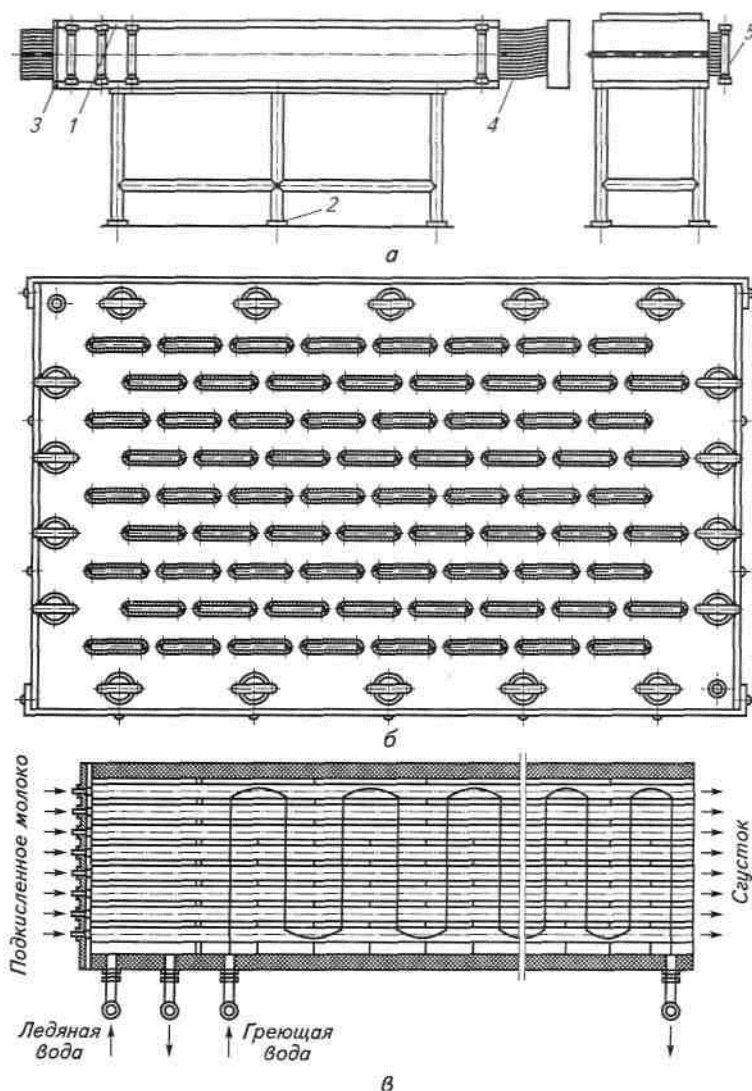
Трубчатый коагулятор: а - общий вид: 1 — корпус; 2— станина; 3— передняя крышка; 4— задняя крышка; 5 — коллектор; б — расположение каналов в коагуляторе; в — схема движения греющей воды в рубашке коагулятора
